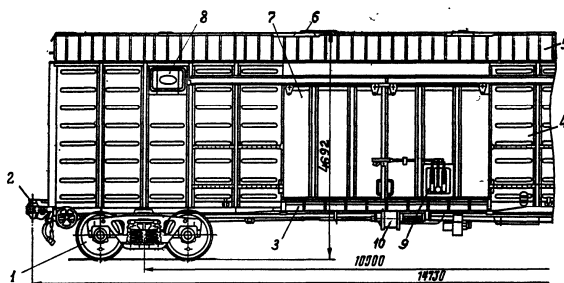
Чотиривісний критий металевий вагон з розширеними дверними отворами
